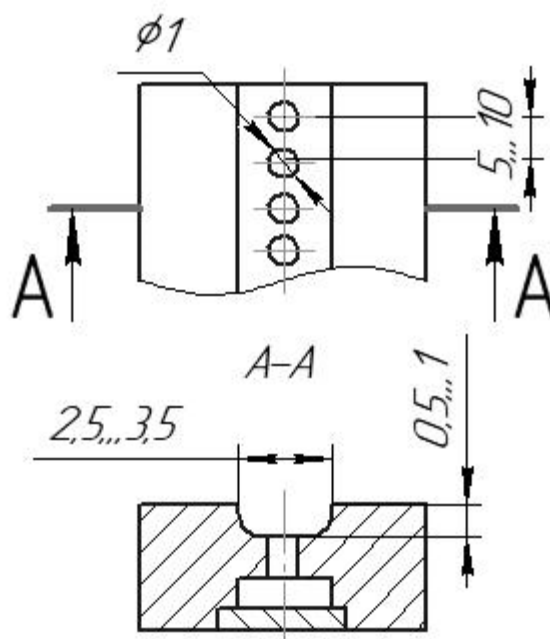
Формуюча підкладка для захисту зворотної сторони (кореня) шва
